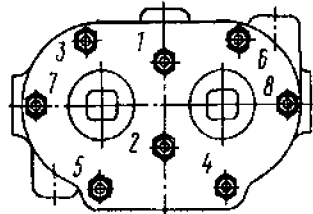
Порядок затяжки гаек шпилек крепления головки компрессора
